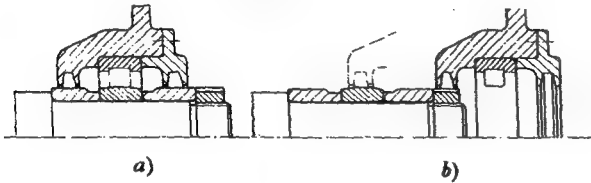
Ejemplos de montaje a) y de desmontaje b) de un cojinete de forma abierta.
